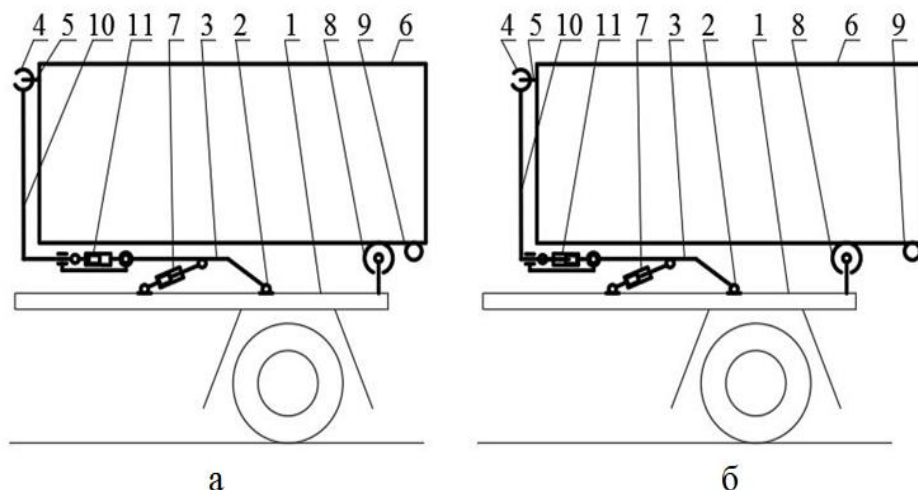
Спрощена конструктивна схема гакового навантажувача з телескопічною базовою рамою: а) в початковому положенні; б) зі зрушеною гаковою рамою.
